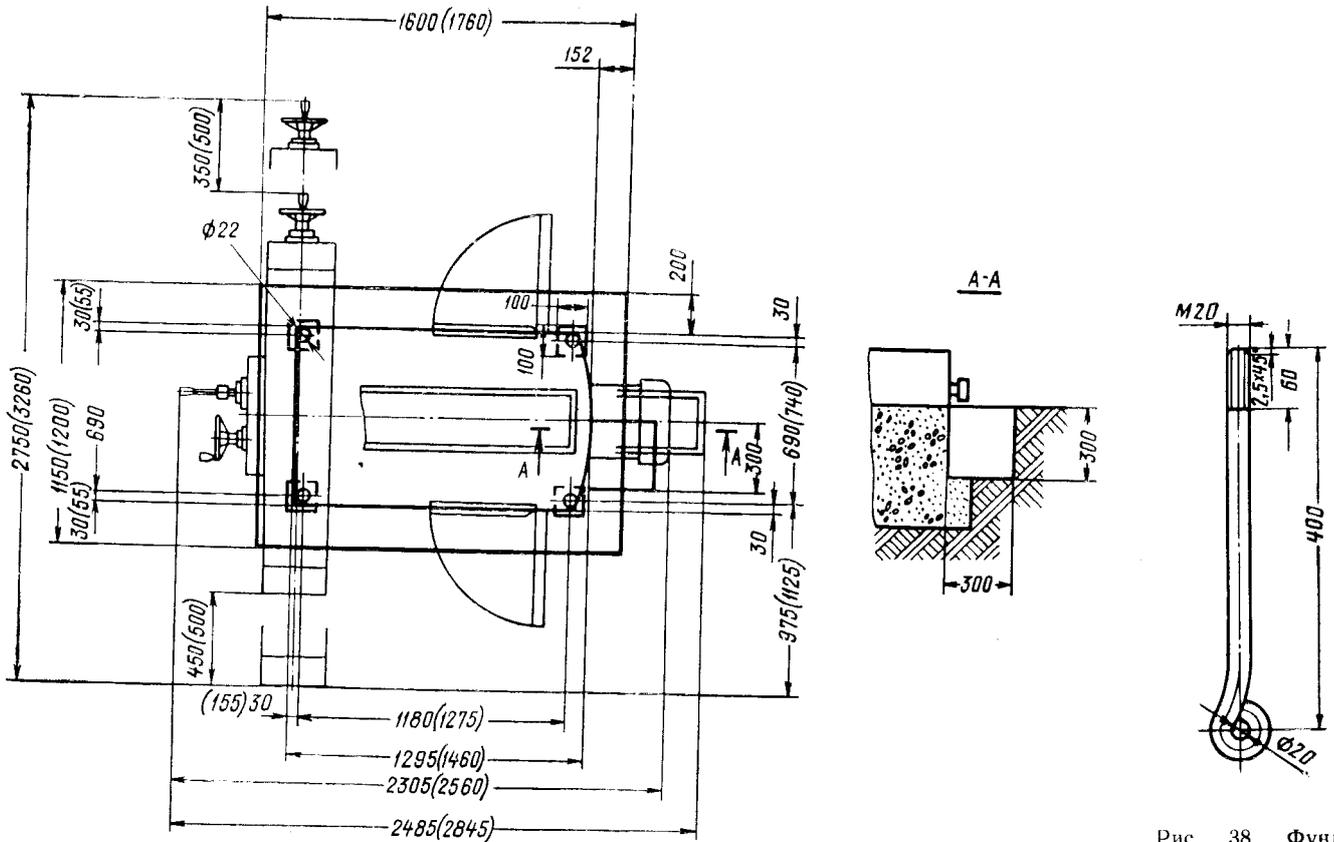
Установочный чертеж станков 6P82Г, 6P83Г (размеры в скобках приведены для станка 6P83Г)
